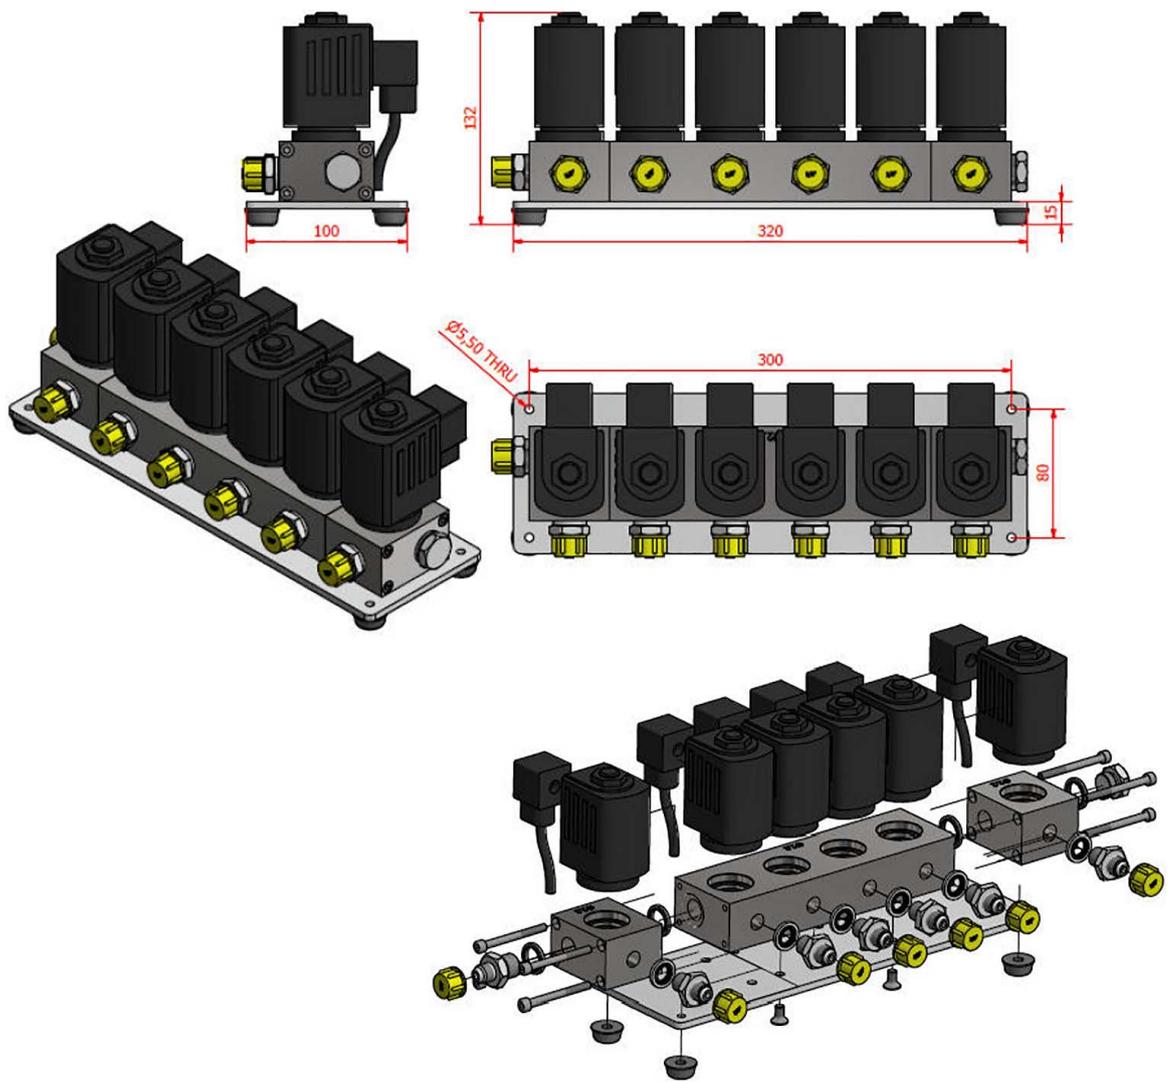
Dimensions du bloc de vannes 5+1 INDUCT (en mm)
